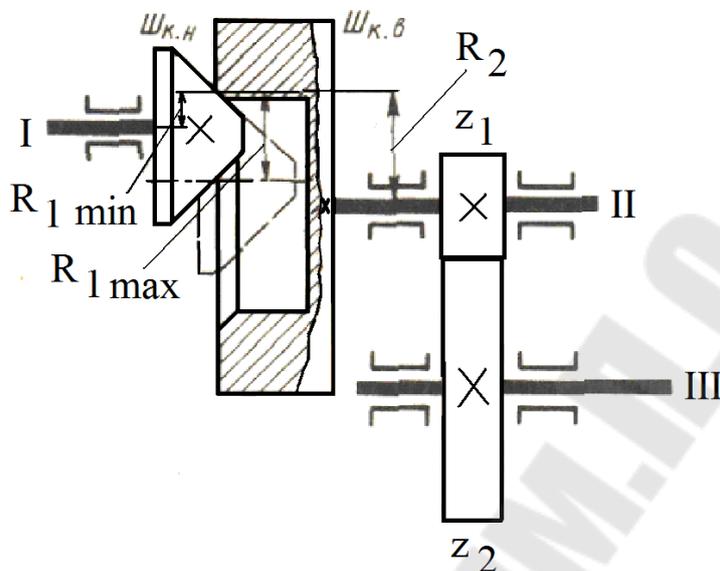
Схема вариатора с наружным и внутренним коническими шкивами
